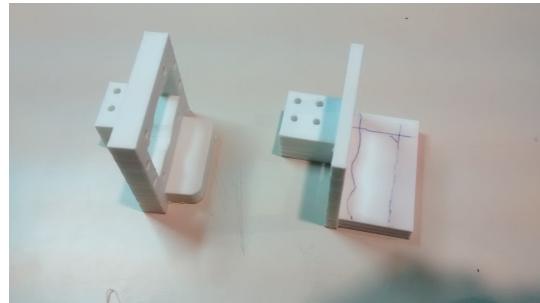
Foto de pieza de sujeción del motor de la herramienta.
